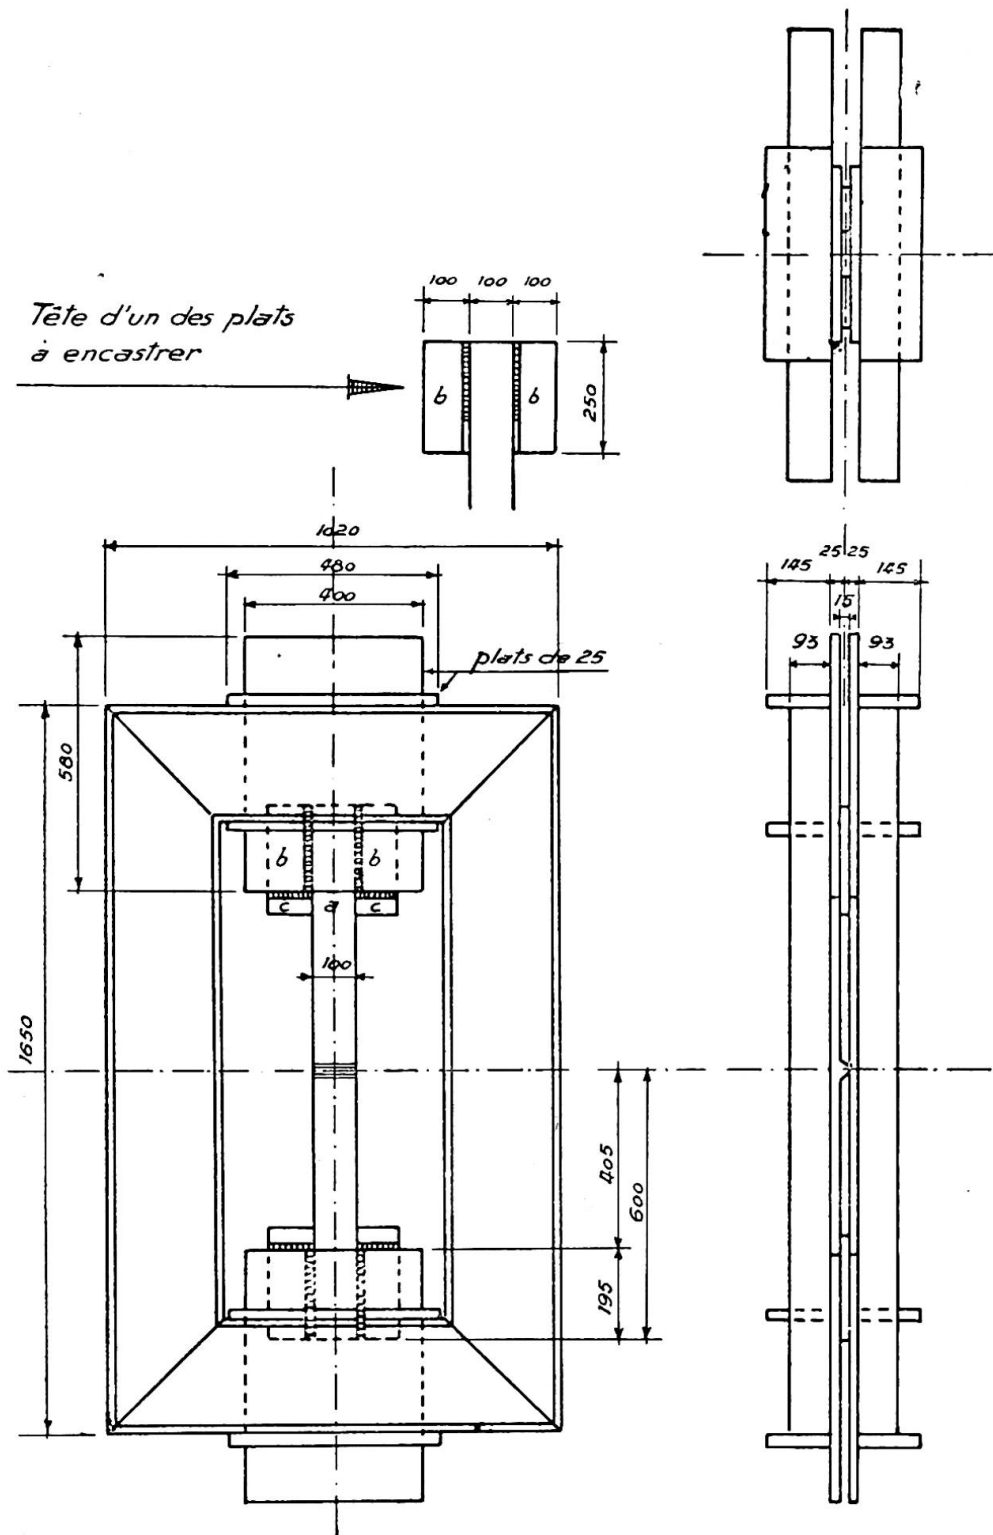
Cadre rigide pour l'encastrement des éprouvettes.
